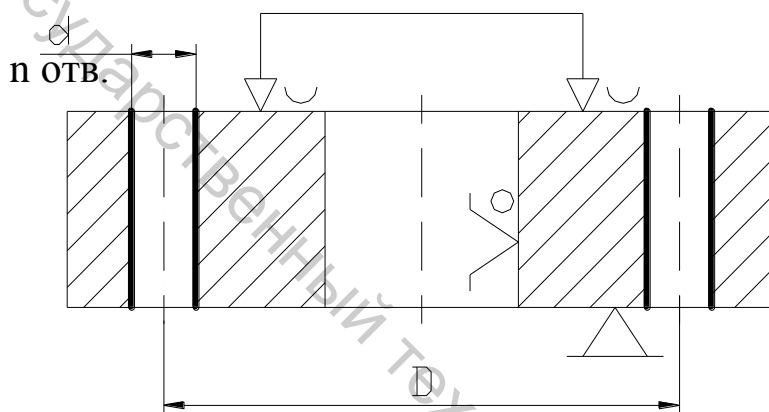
Схема установки заготовки в самоцентрирующих тисках с призматическими губками
